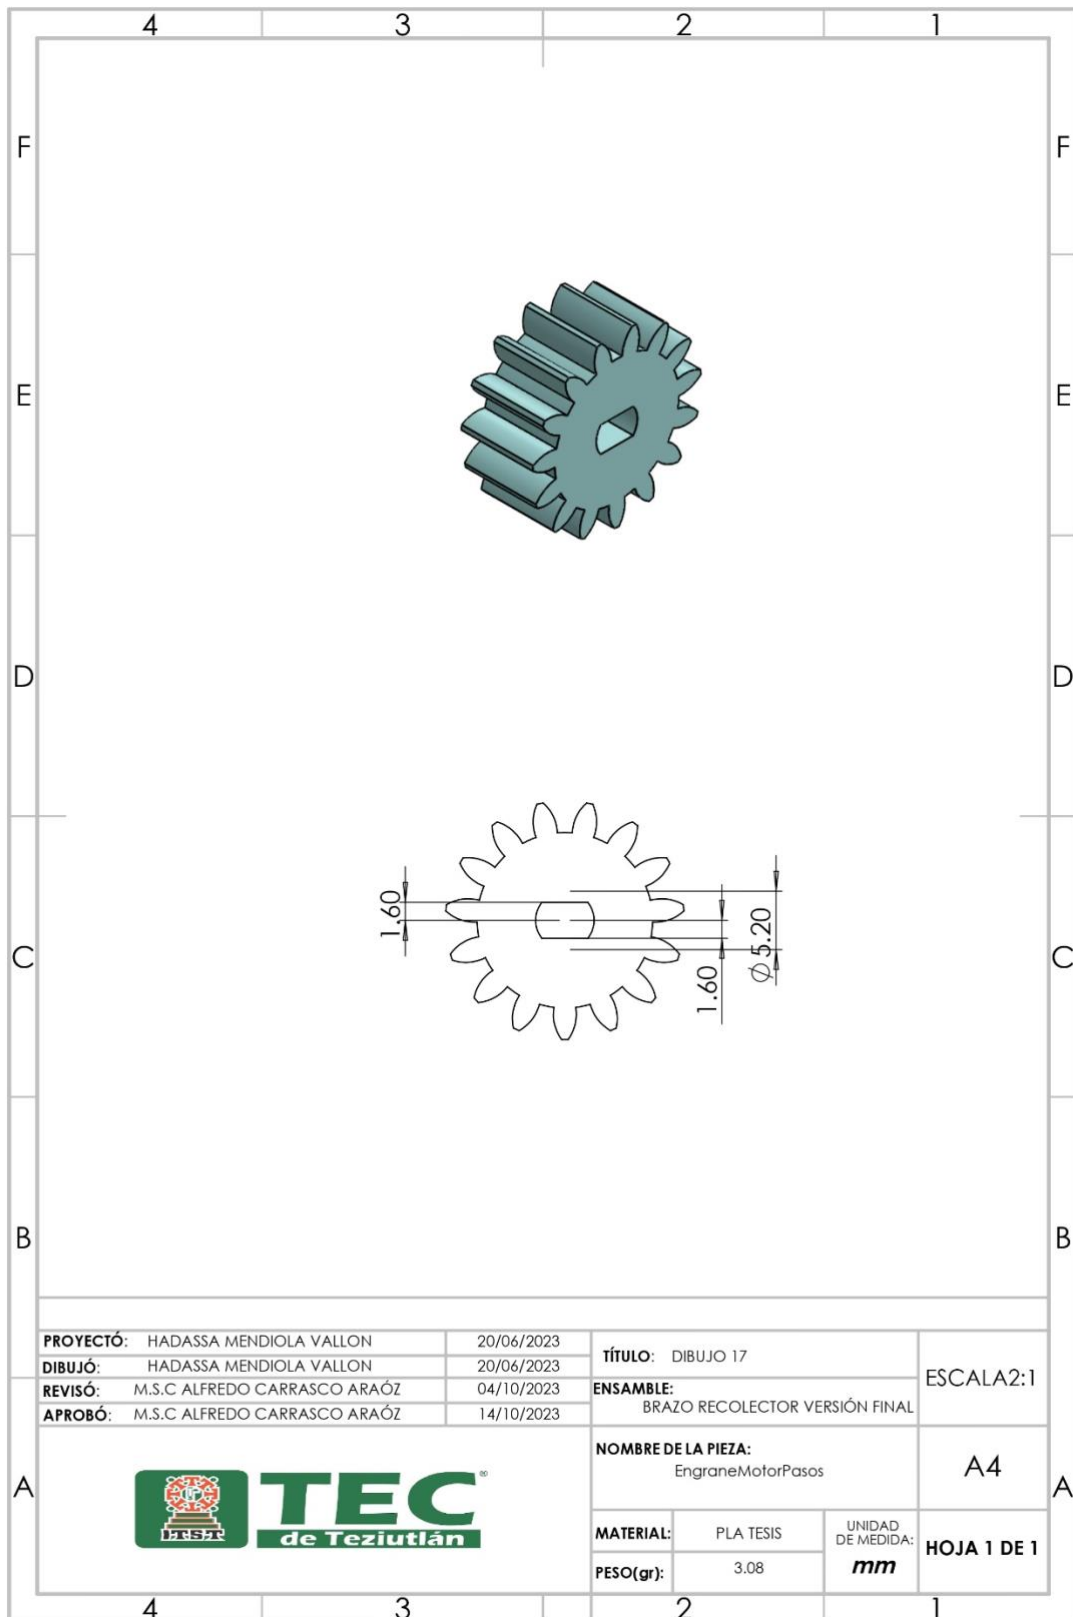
Dibujo en SolidWorks "Engrane Motor a Pasos". Autor propio
